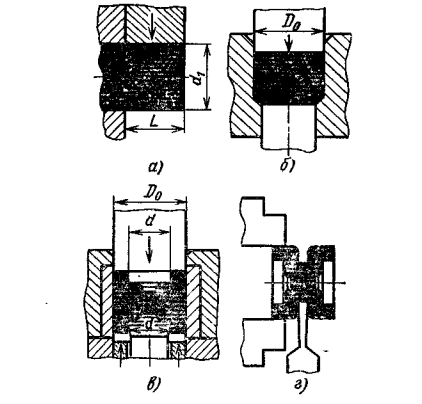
Технологические переходы штамповки спаренной штампованной заготовки корпусов карданных подшипников: а — отрезка в штампе; б — полузакрытая осадка (калибровка); в — двухстороннее выдавливание; г — разрезка на токарном автомате
